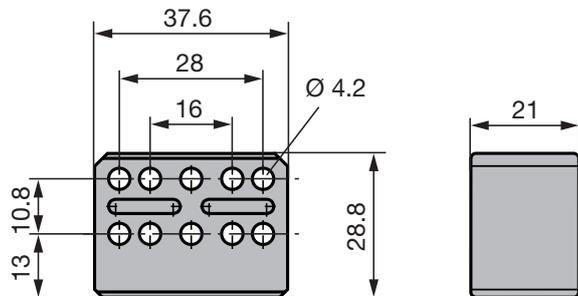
Dimensions de montage du capteur de position BTL6-A-3800-2
